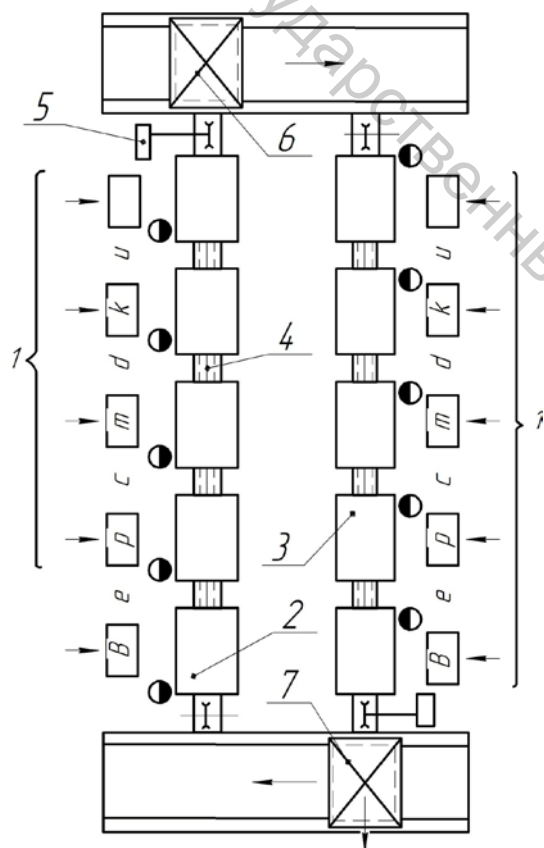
Схема планировки сборочного участка на подвижных тележках: 1 – зона подачи деталей и узлов; 2 – начало сборки; 3 – тележка; 4 – цепь конвейера; 5 – привод конвейера; 6 – передача объекта на другую ветвь конвейера; 7 – выдача собранного изделия
